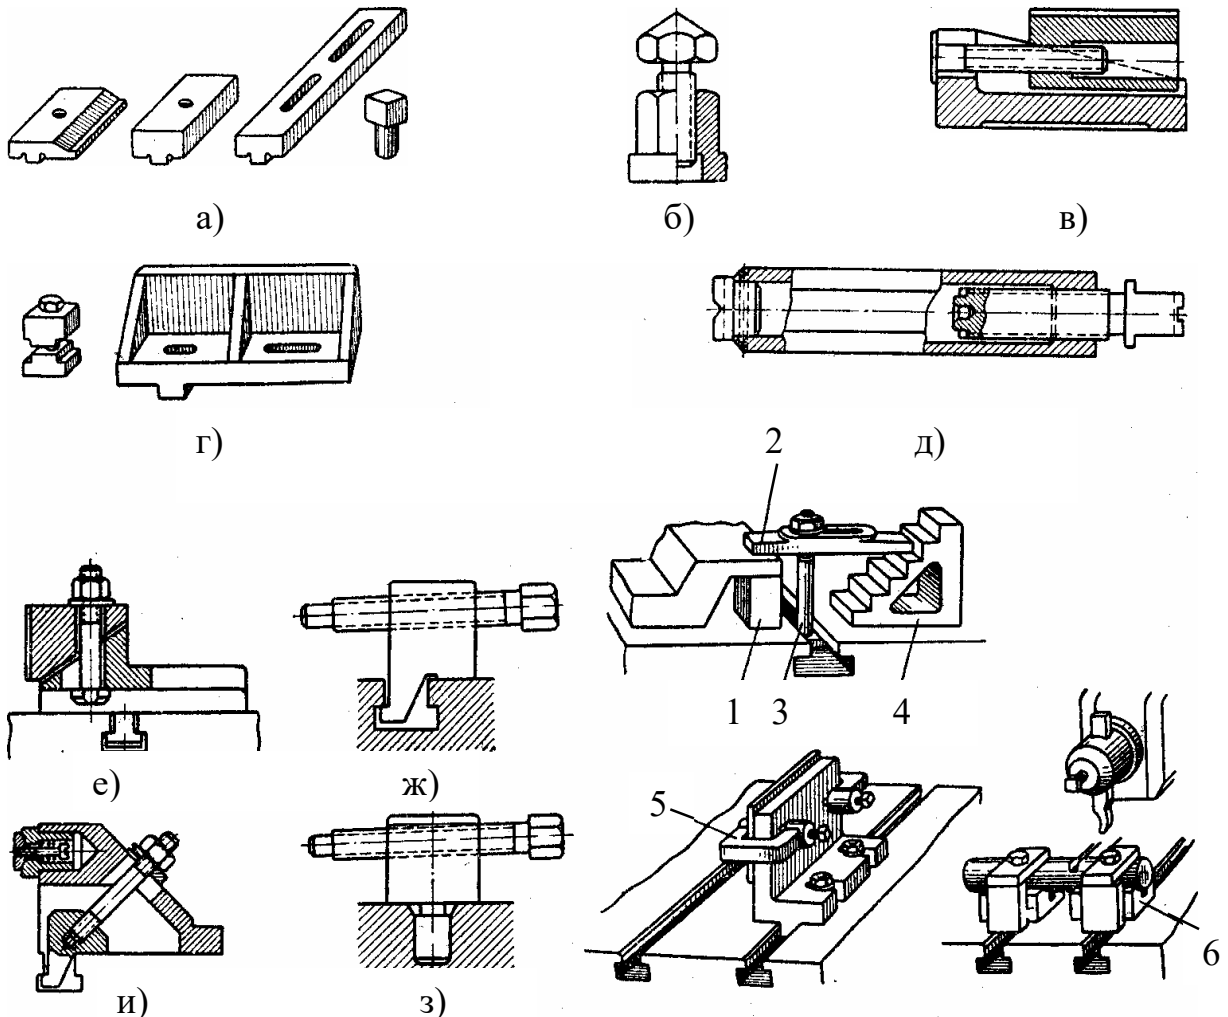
Кріпильні пристосування: а – упорні планки та колодки; б - гвинтовий домкрат; в – клиновий домкрат; г – упорний кутник; д – розпирний гвинт; е – клиновий притискач; ж, з – гвинтові притискачі; и – притискач зі сферичною п'ятою; 1 – підставка; 2 - прихоплювач; 3 – кріпильний болт; 4 – східчаста опора; 5 – струбцина; 6 - призма
